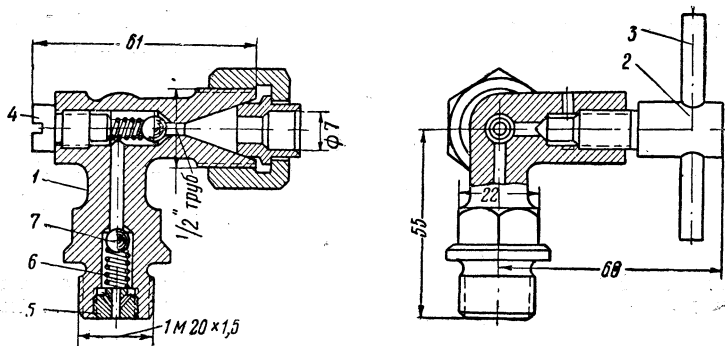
Обратный клапан шарового типа черт. № П-32-250-105сб
